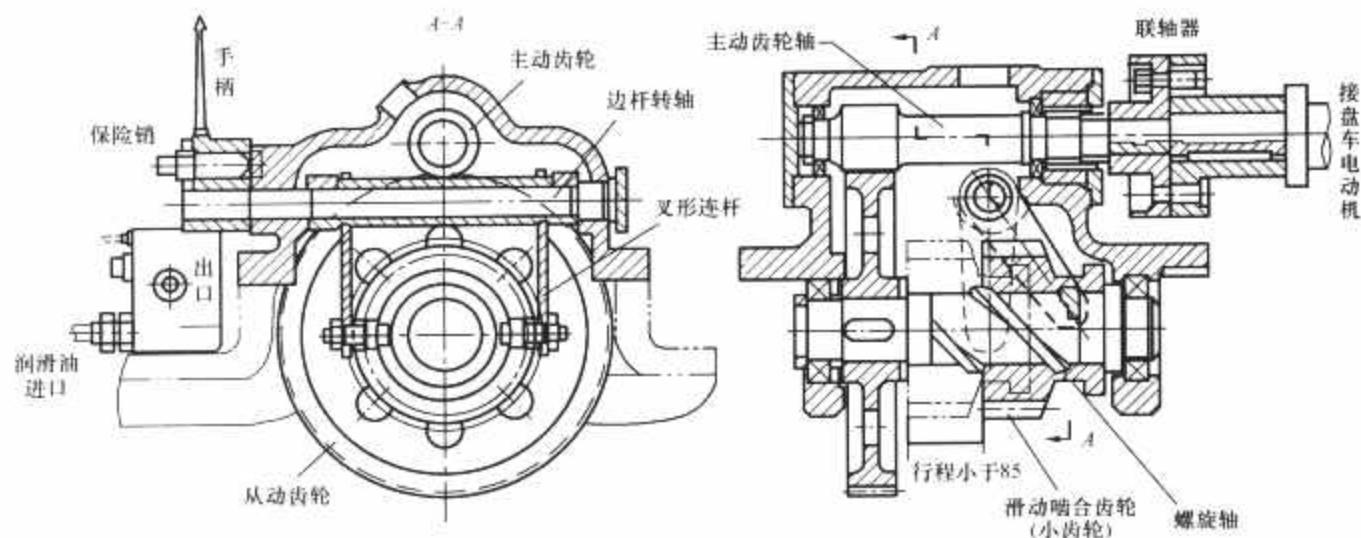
螺旋轴齿轮传动式盘车装置的典型结构
